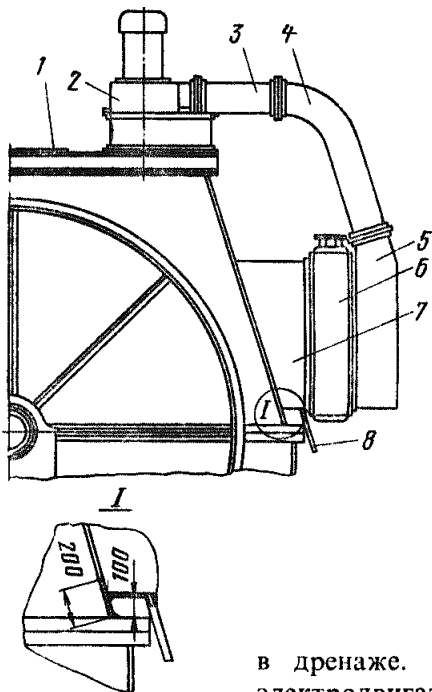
Общий вид электродвигателя СДСЗ-2000-100 с охладителем ВУП-16 × 6 × 1500.4 после реконструкции (чертеж № ОБГ.301.000):
